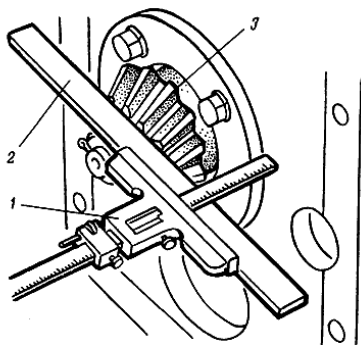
Проверка установочной высоты ведущей шестерни главной передачи: 1 - штангенглубиномер; 2 - линейка; 3 - ведущая шестерня
